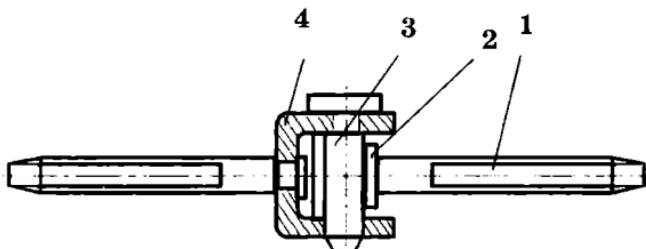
Ввертные дверные петли: 1 — стержень петли; 2 — гайка; 3 — центральный болт; 4 — скоба поворотного стержня
